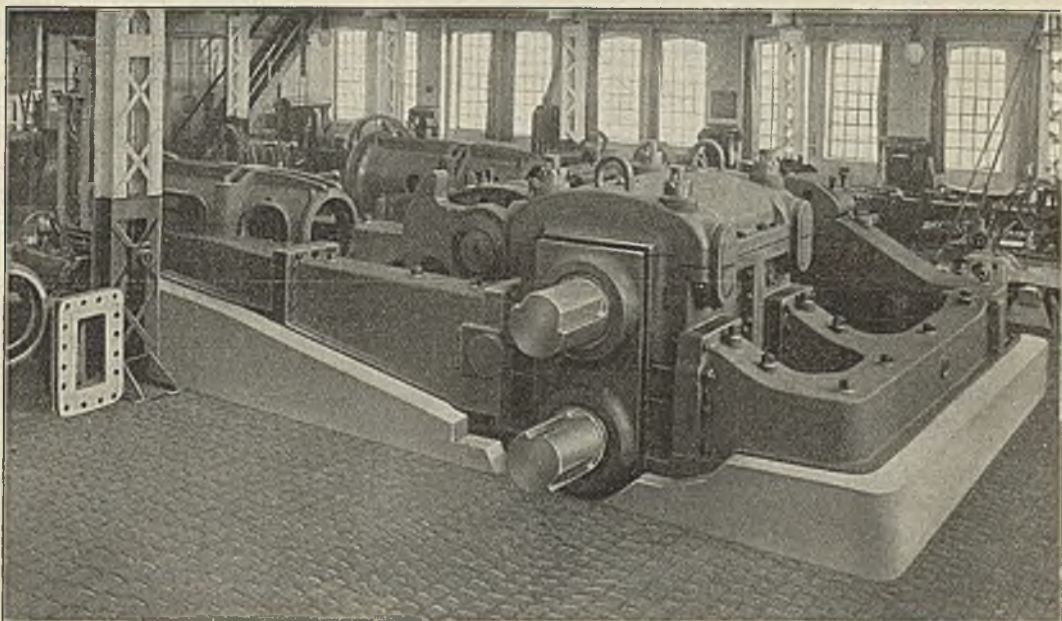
Zwillings-Tandem-Reversier-Maschine mit eingebautem Kammwalzgerüst, System Ortmann.
